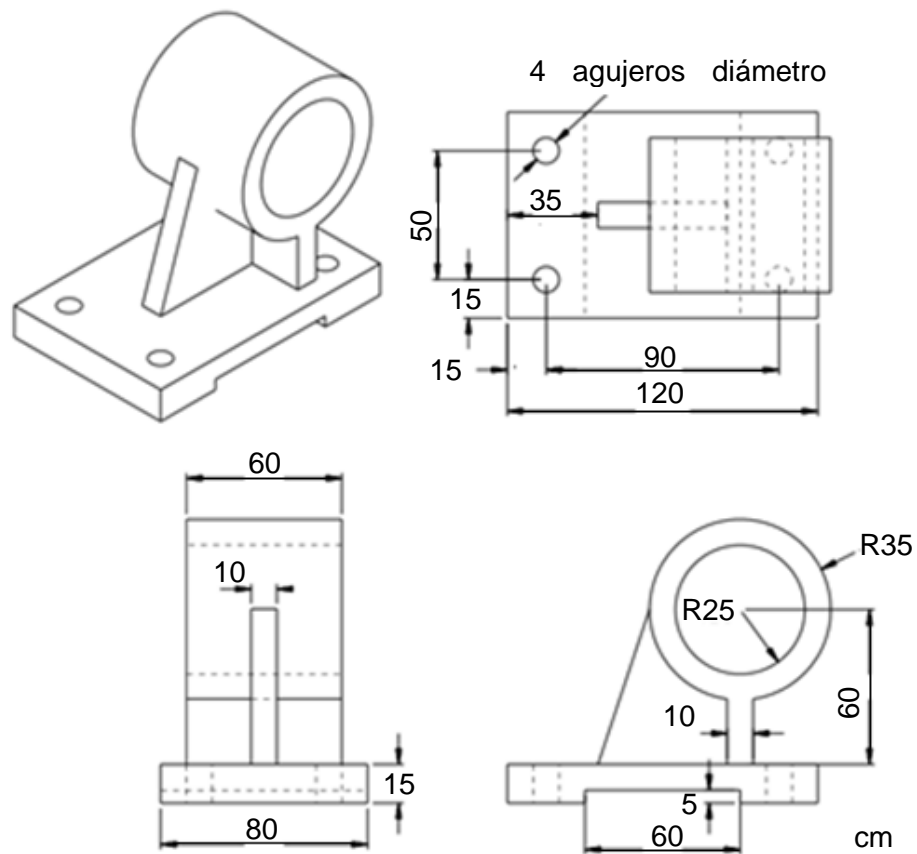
Soporte tubular para sistema transmisión de gas de alta presión.
